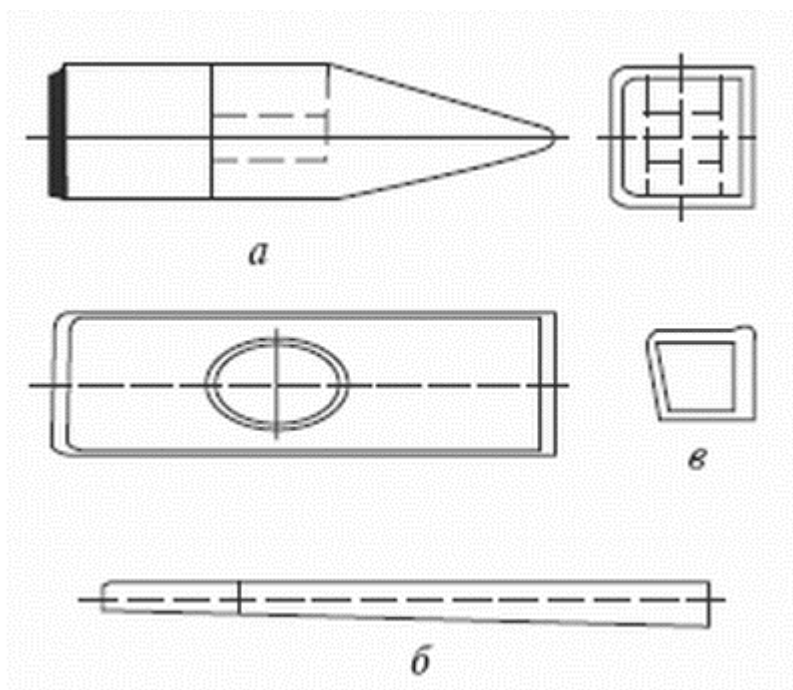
Слесарный молоток: а – металлическая головка; б – рукоятка; в – клин
